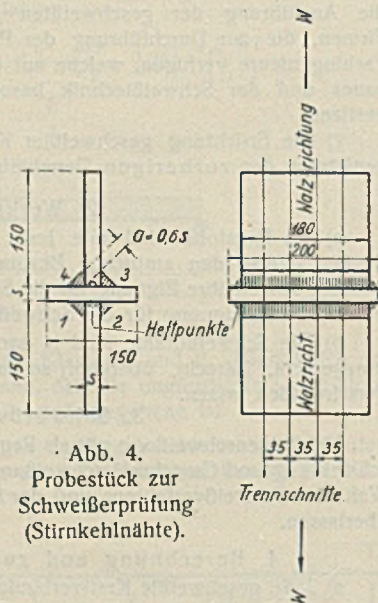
Probestück zur Schweißerprüfung (Stirnkehlnähte).
